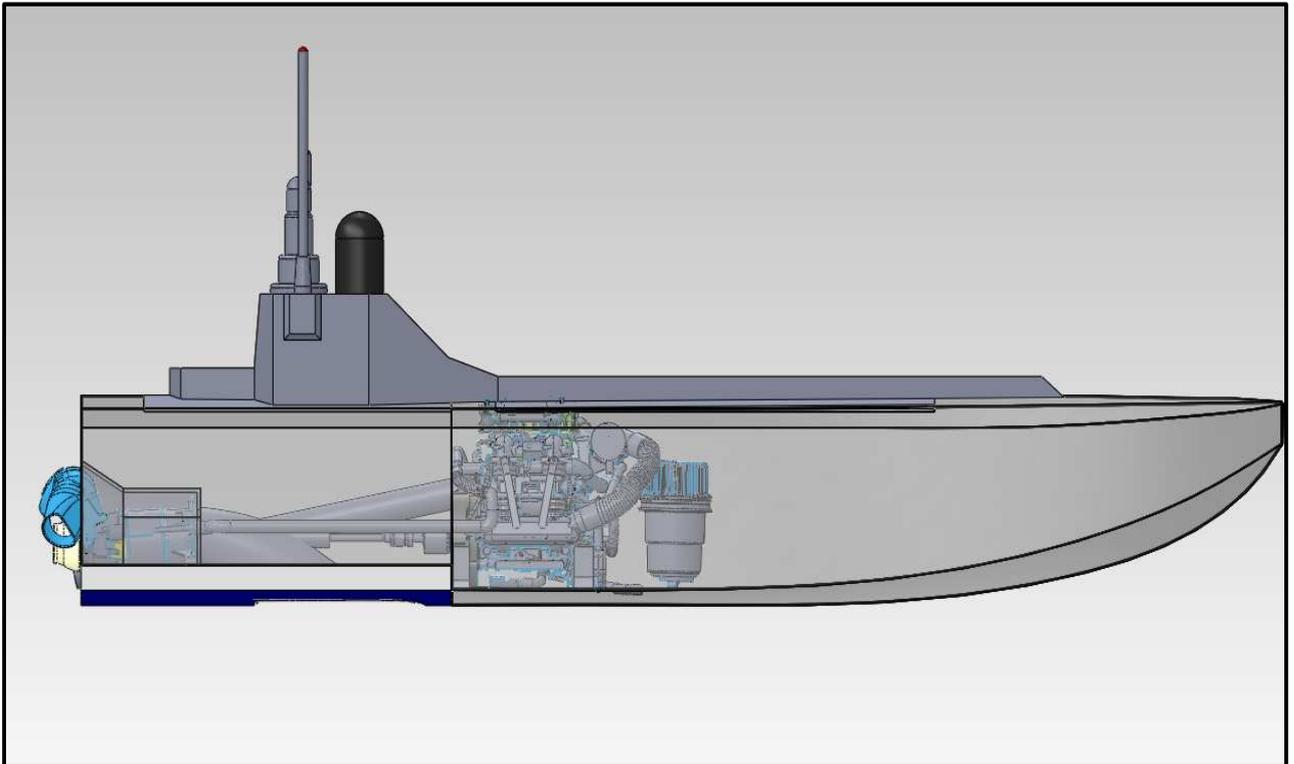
Einbauposition des Motors, Seitenansicht
